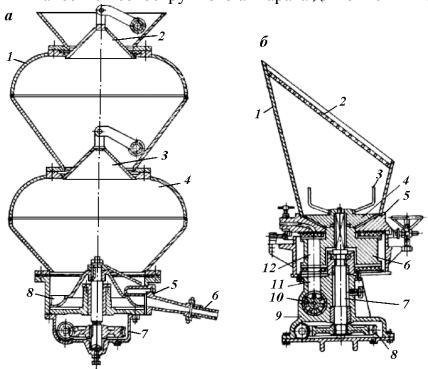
Конструкции цемент-пушек (вертикальный разрез):
